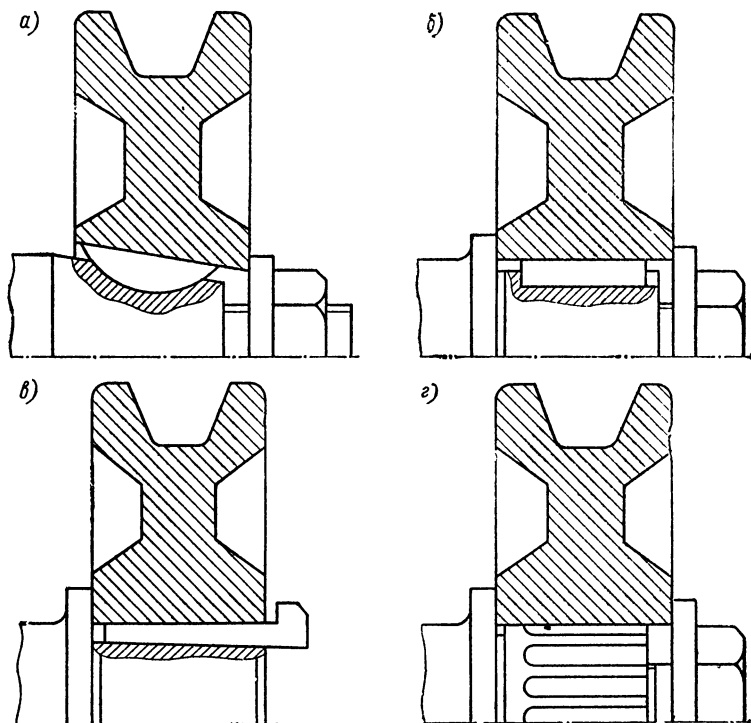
Способы установки шкивов на валу: а...в — на шпонки; г — на шлицы
